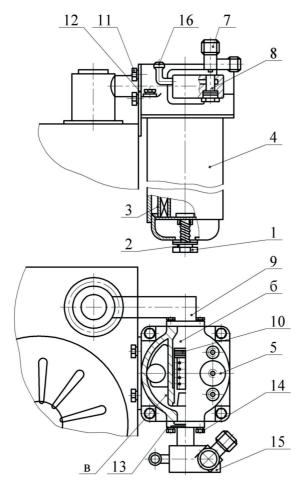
Установка фильтра: 1 — заглушка; 2 — прокладка; 3 — фильтроэлемент; 4 — фильтр; 5 — указатель давления; 7 — тройник; 8 — обратный клапан; 9 — подвод; 10 — перепускной клапан; 11 — болт; 12 — кронштейн; 13 — кольцо; 14 — болт; 15 — распределитель; 16 — угольник
